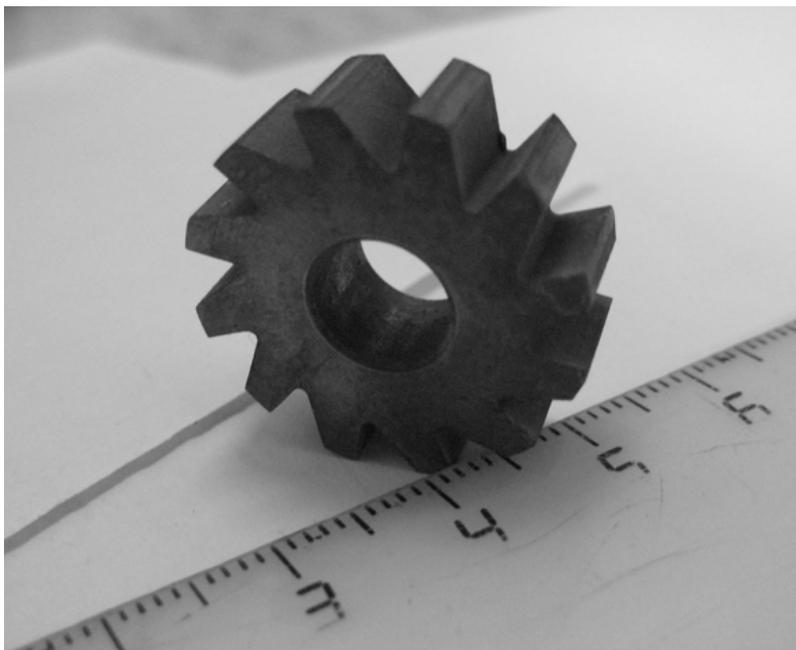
Заготовка мелко модульной твердосплавной червячной фрезы с вырезанными стружечными канавками на электроэрозионном станке.
